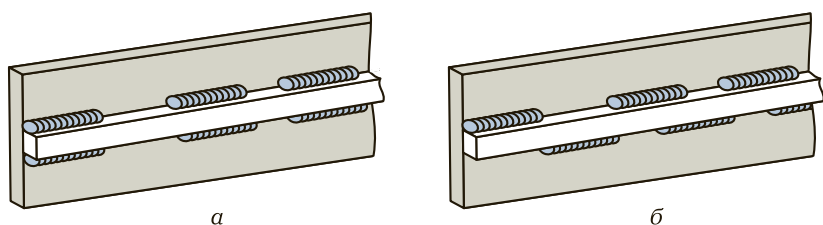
Цепной прерывистый (а) и шахматный прерывистый (б) швы
